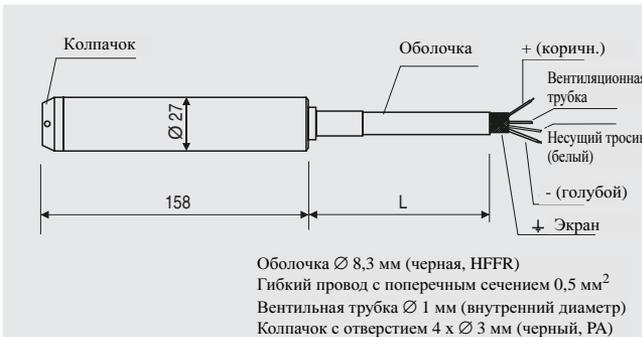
/9 Измерительный преобразователь избыточного давления 7MF1570, размеры
